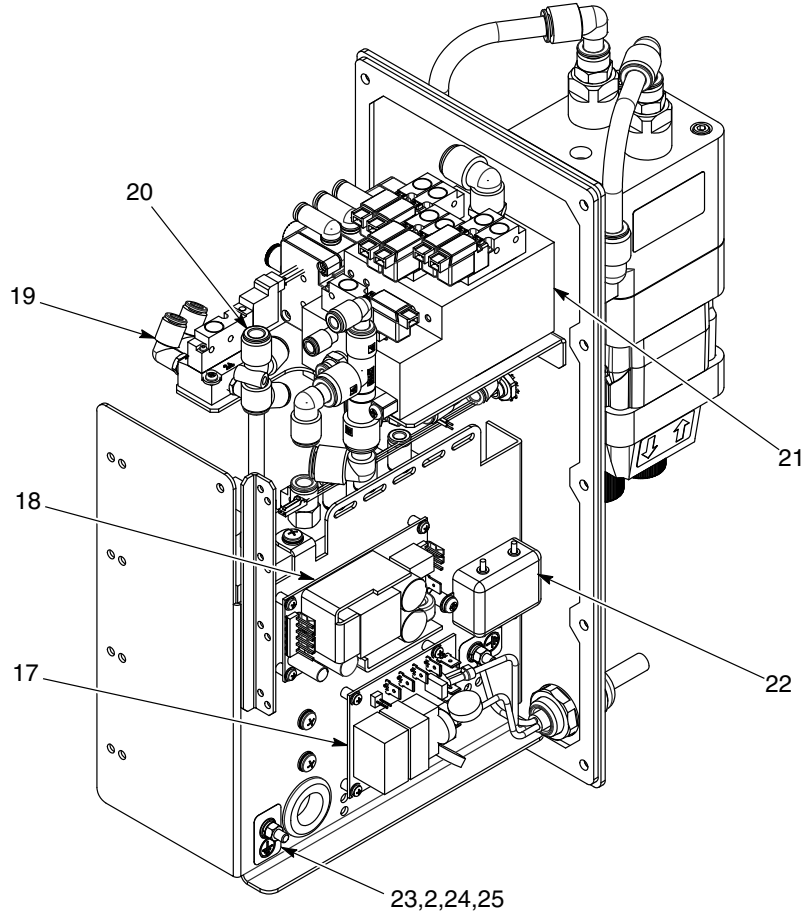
Panel Montaj Grubu Parçaları (2 / 3)
